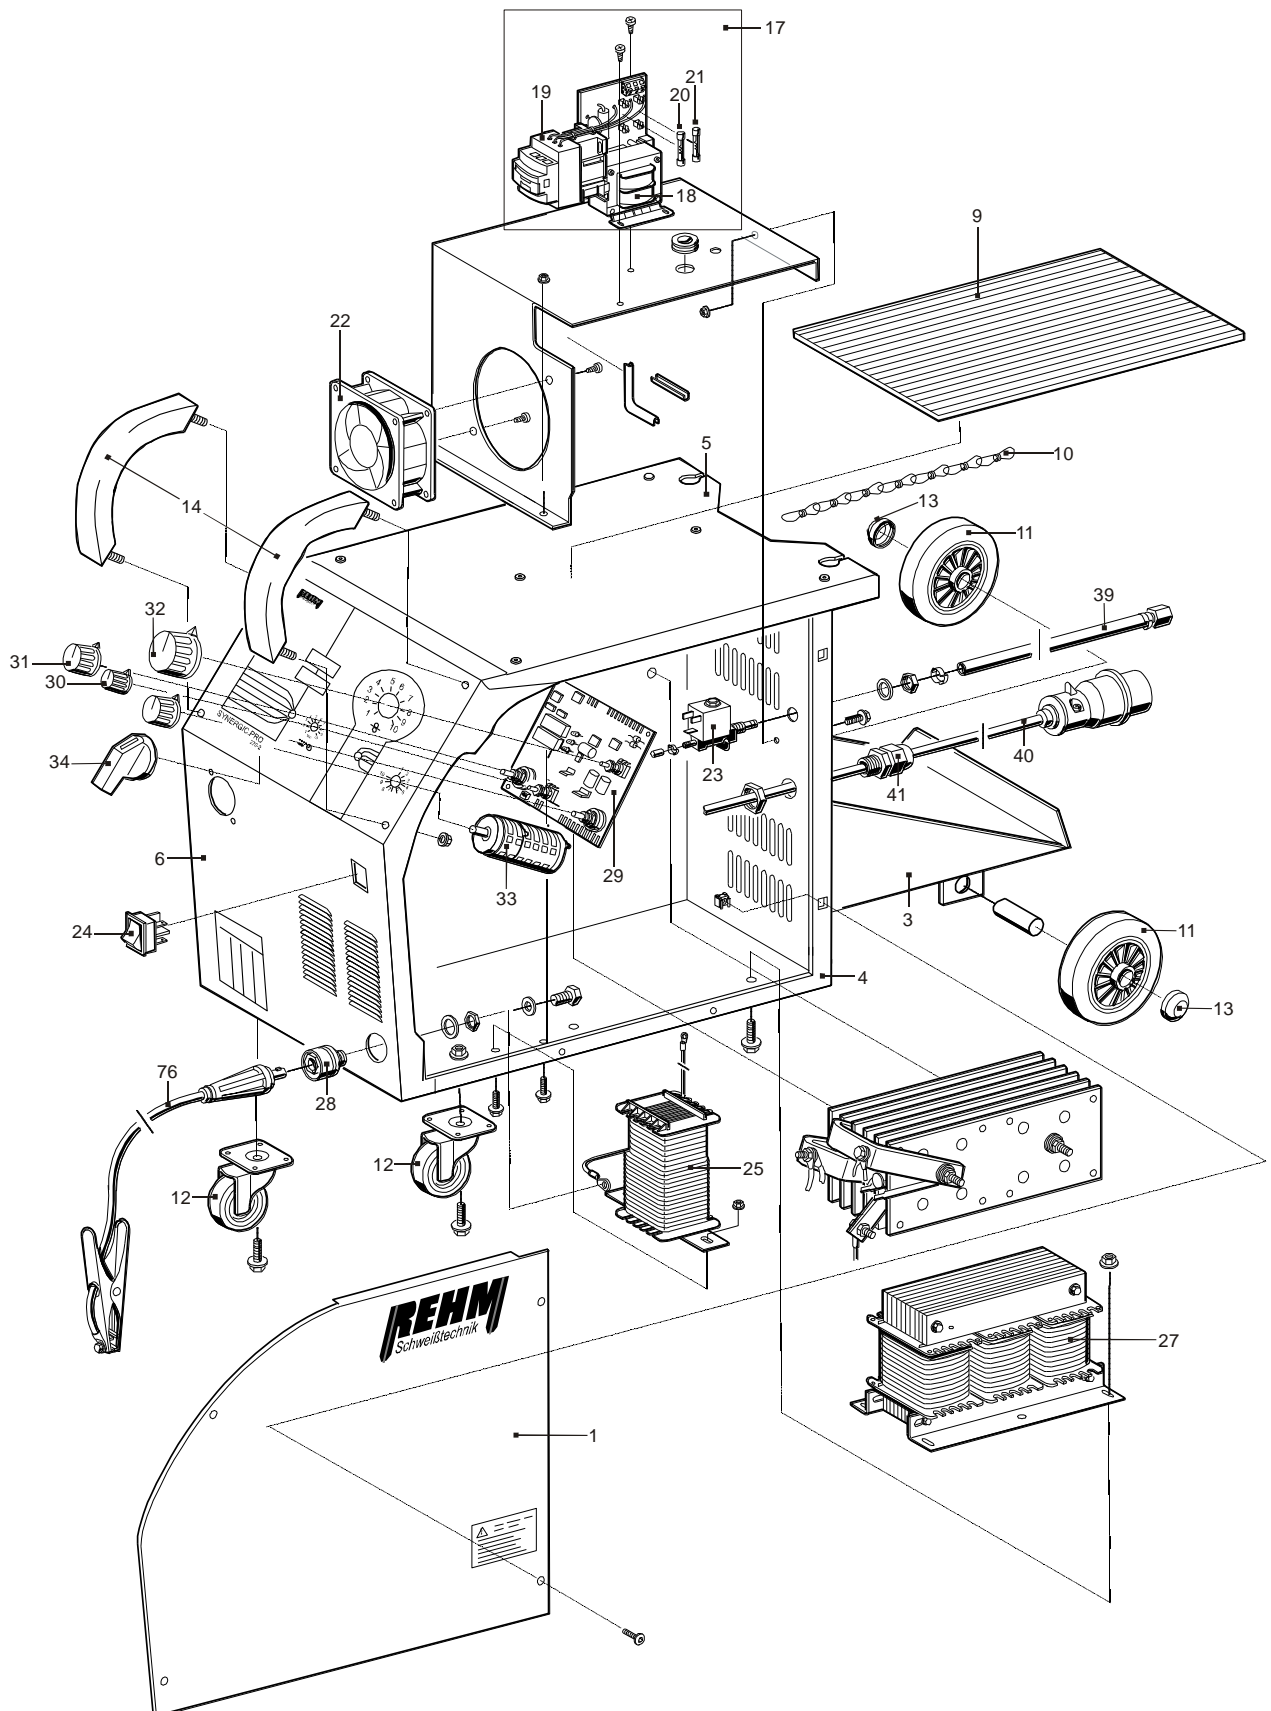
Explosionszeichnung SYNERGIC.PRO² 170-2 – 310-4 (rechts)
